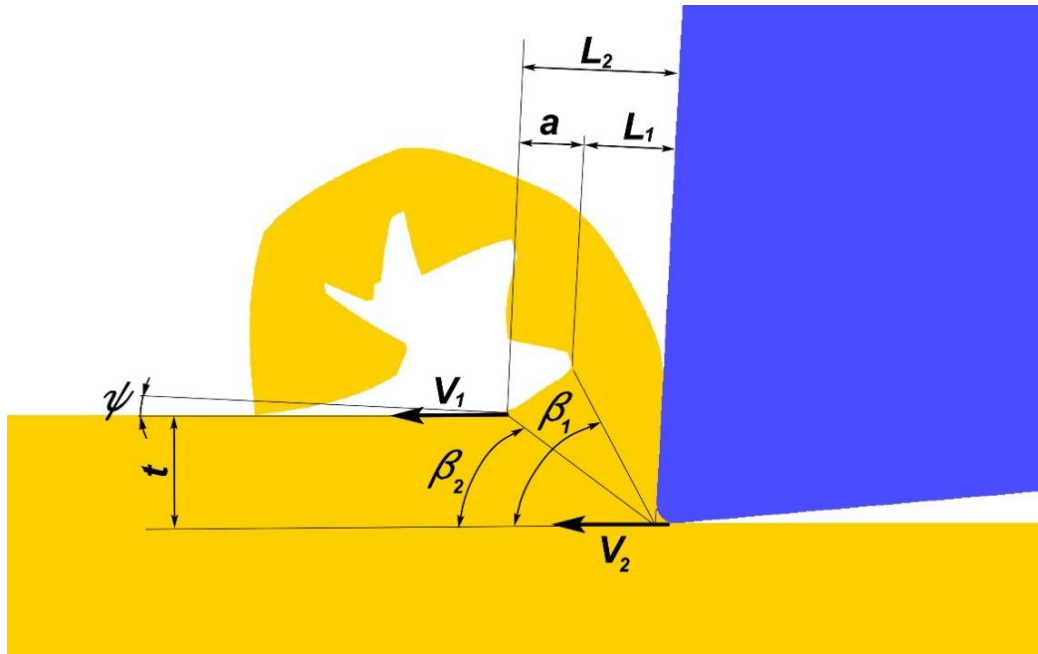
Розрахункова схема формоутворення стружкового елемента під час оброблення титанового сплаву
